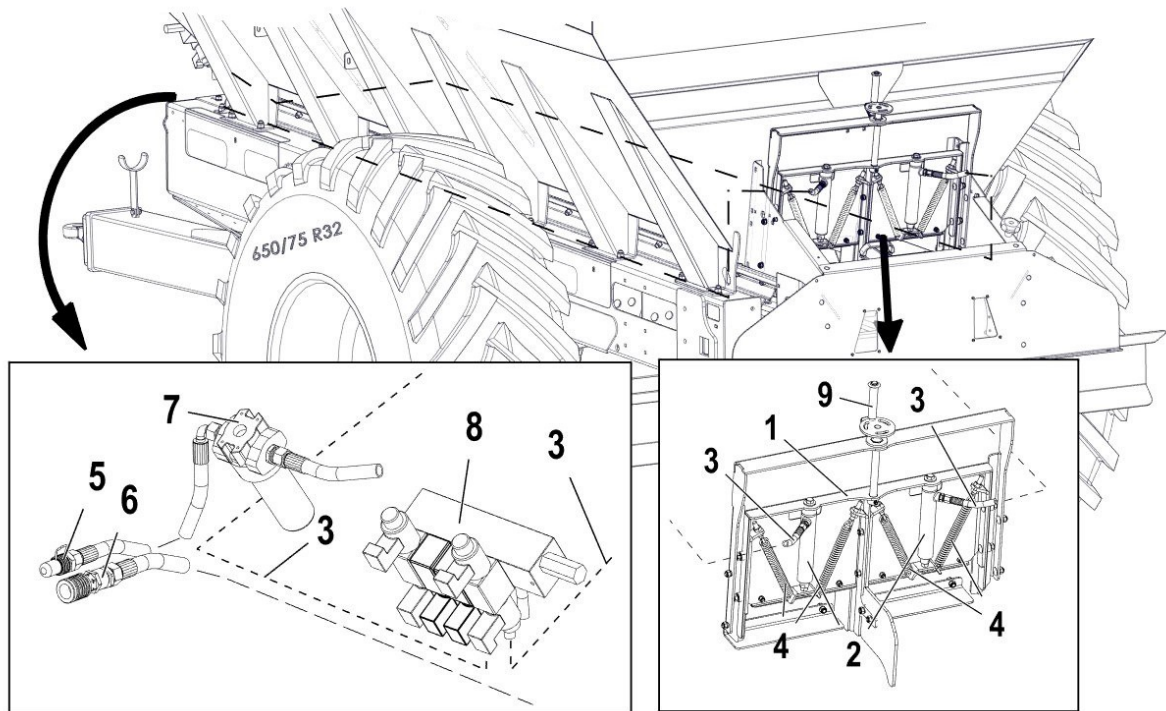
Задвижка для плунжера – иллюстративный вид
